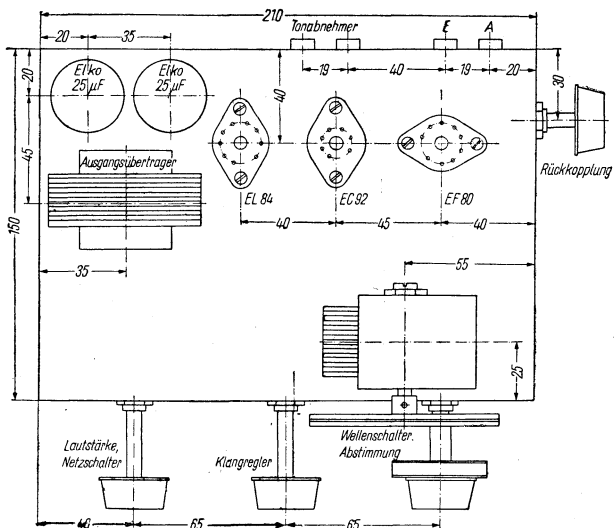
Maßskizze für die Abmessungen und die Bohrungen des Chassis
